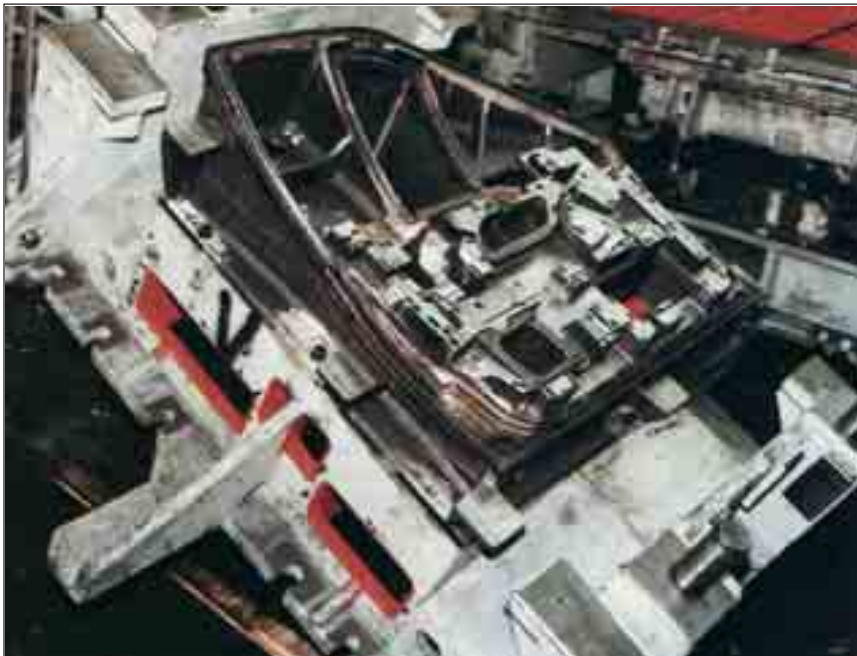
Schnittwerkzeug aus G47CrMn6 (1.7140) zum Herstellen von Karosserieteilen für Pkw
